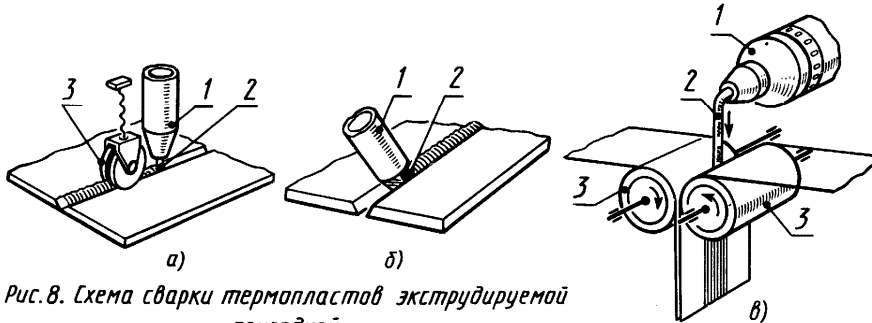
Схема сварки термопластов экструдированной присадкой
